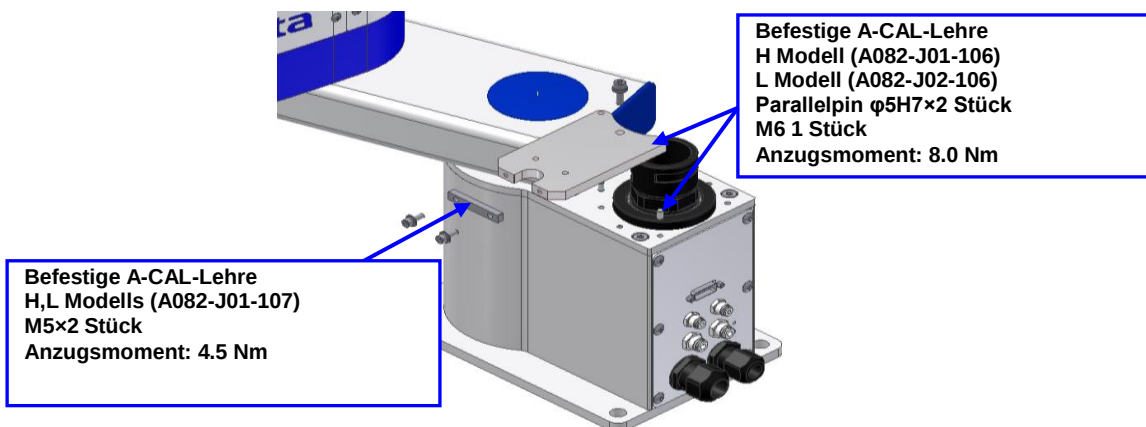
Einzelteilzeichnung A-CAL-Lehre Befestigung
